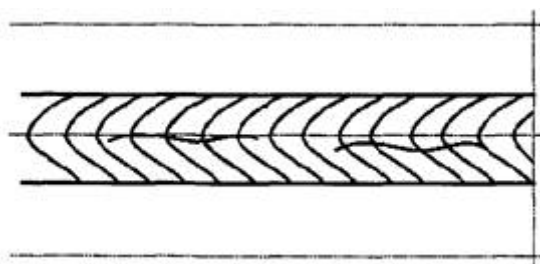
Разветвленная трещина сварного соединения
